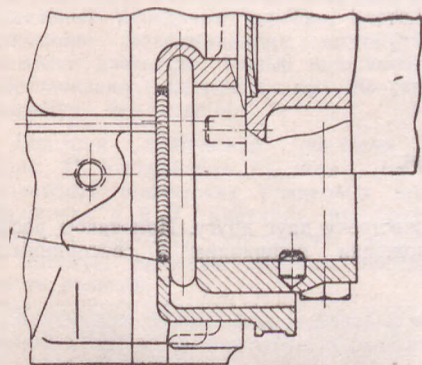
Уменьшение диаметра пояса крышки заднего подшипника и блока при помощи наварки металла.
